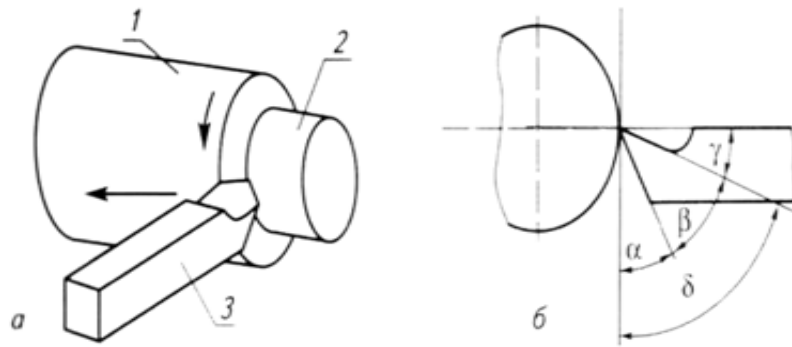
Схема процесса точения (а): 1 – обрабатываемая поверхность; 2 – обработанная поверхность; 3 – резец; основные углы режущей части резца (б): γ – передний угол; α – задний угол; β – угол заострения резца; δ – угол резания
